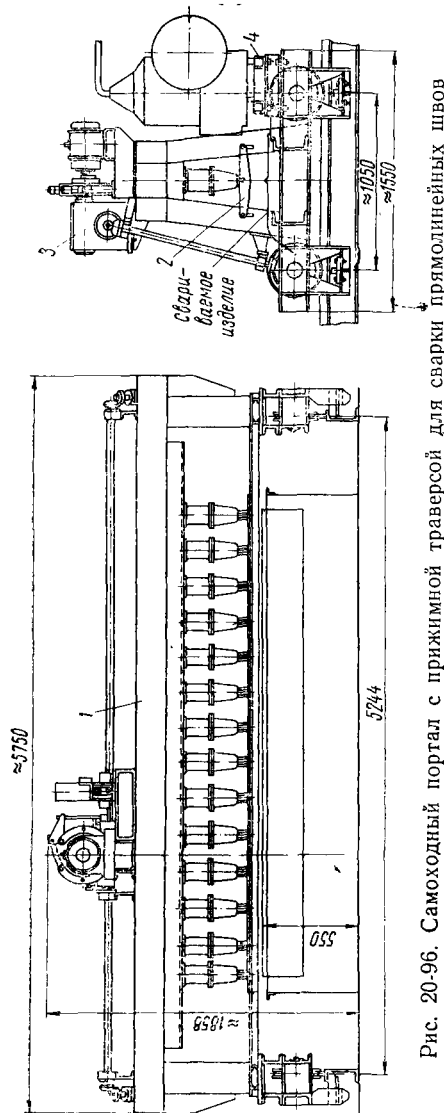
Самоходный портал с прижимной траверсой для сварки прямолнейных швов
